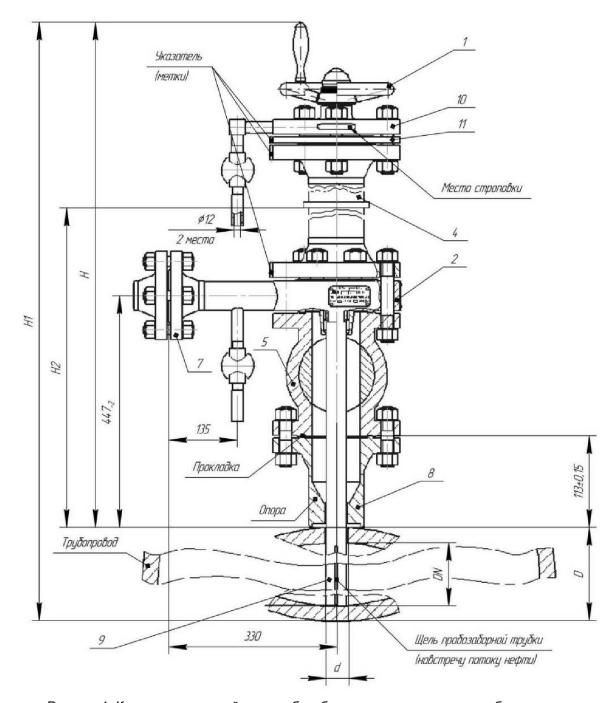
Конструкция устройства пробозаборного щелевого типа с лубрикатором
